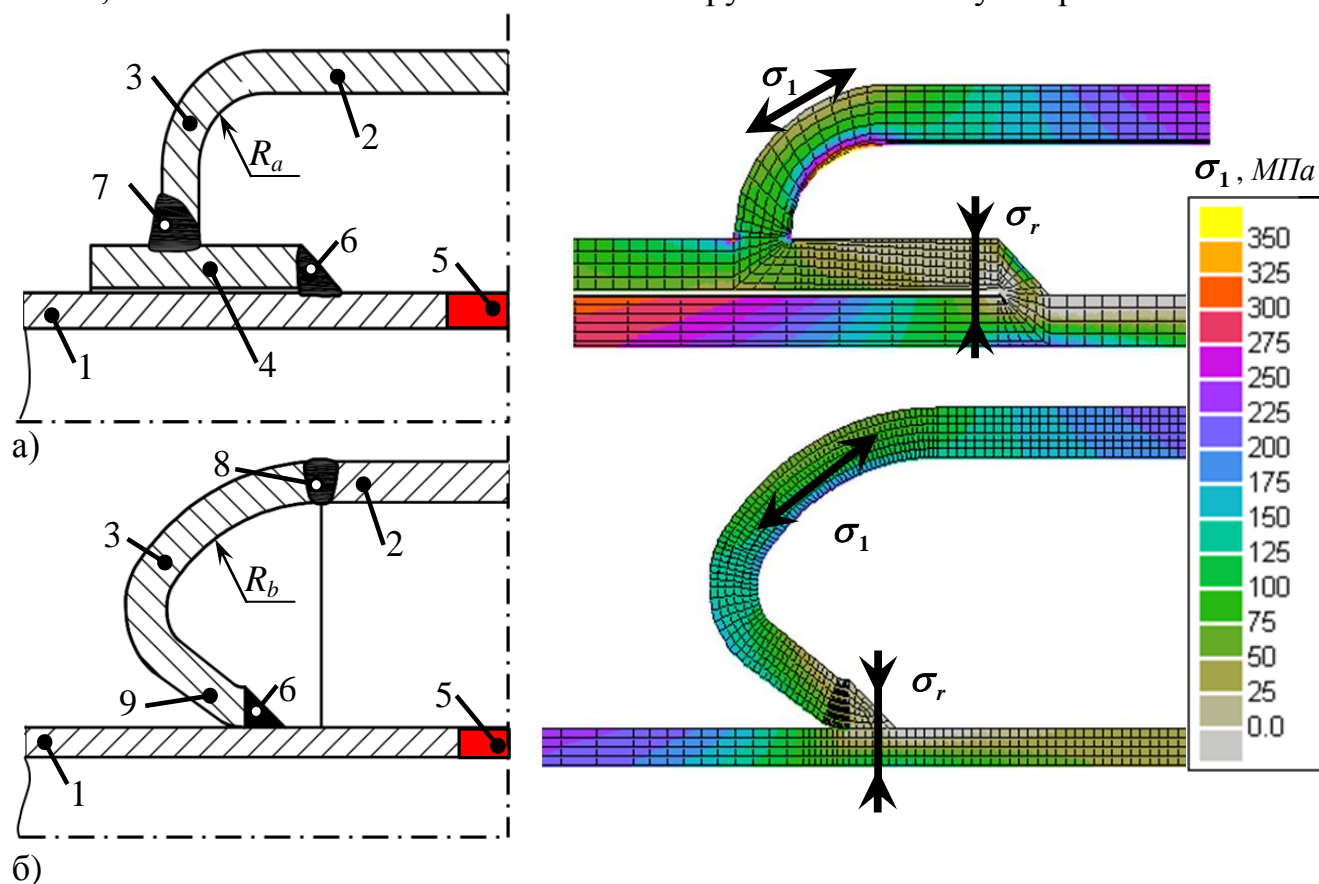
Оформление сварного соединения муфты с трубой и распределение компоненты максимального растягивающего напряжения в прототипе (а) и новой конструкции муфты (б). 1 – труба; 2,3 – цилиндрическая и торовая часть муфты; 4 – подкладное кольцо; 5 – сквозной дефект; 6 – угловой шов; 7 – тавровое соединение; 8 – стыковой шов; 9 – конический участок
